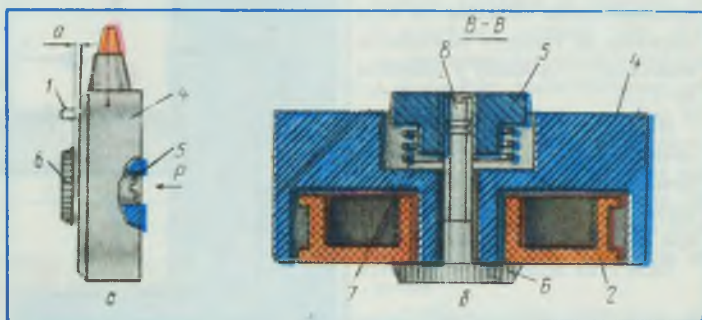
Общий вид зимней удочки: 1 — ручка вращения катушки; 2 — катушка; 3 — хлыстик; 4 — рукоятка-корпус; 5 — втулка; 6 — регулировочный винт.
